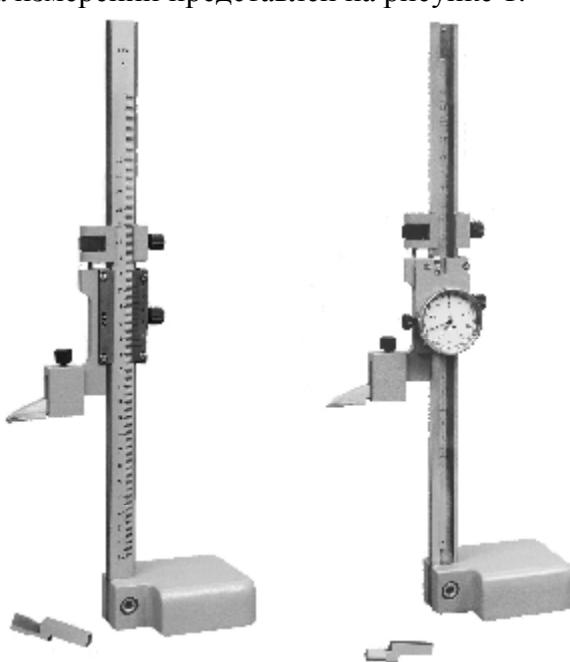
Общий вид штангенрейсмаса ШР, ШРК
